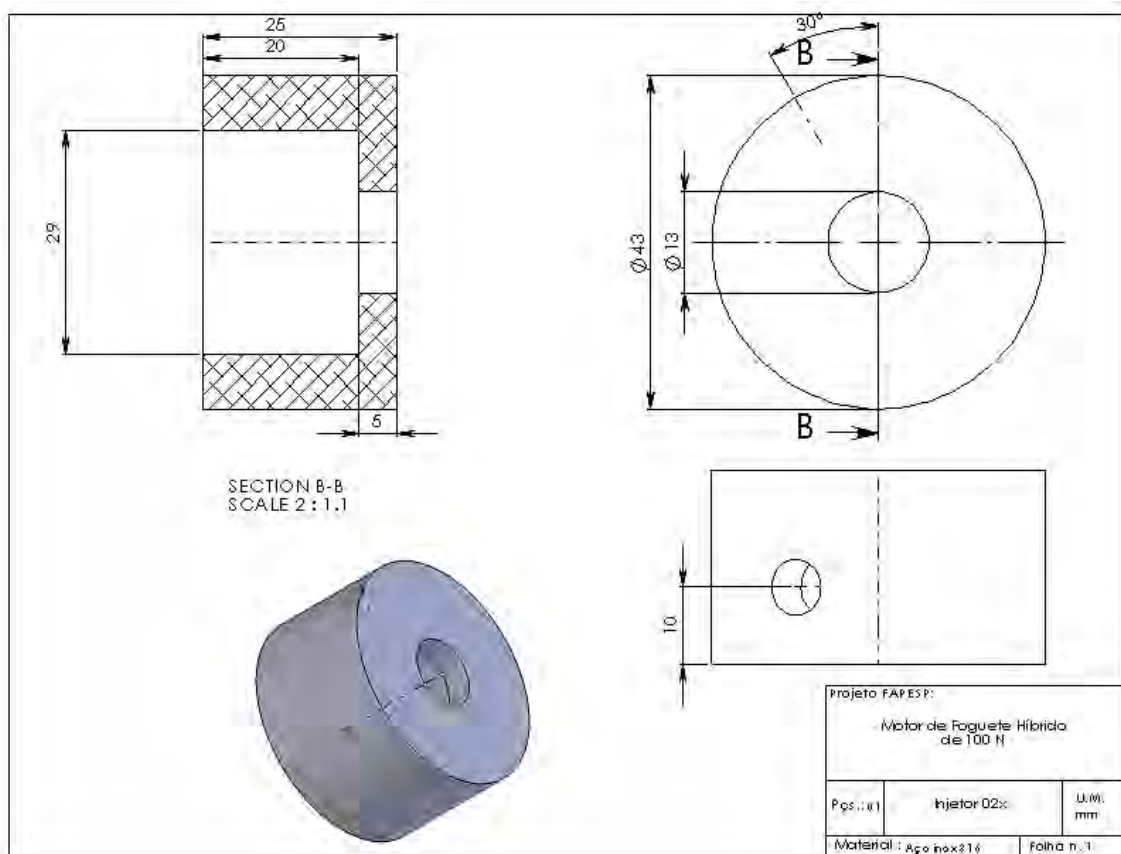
Desmontagem do injetor bipropelente, cotas do cilindro de combustível (UDMH), injetor 02X, para posterior fabricação.
